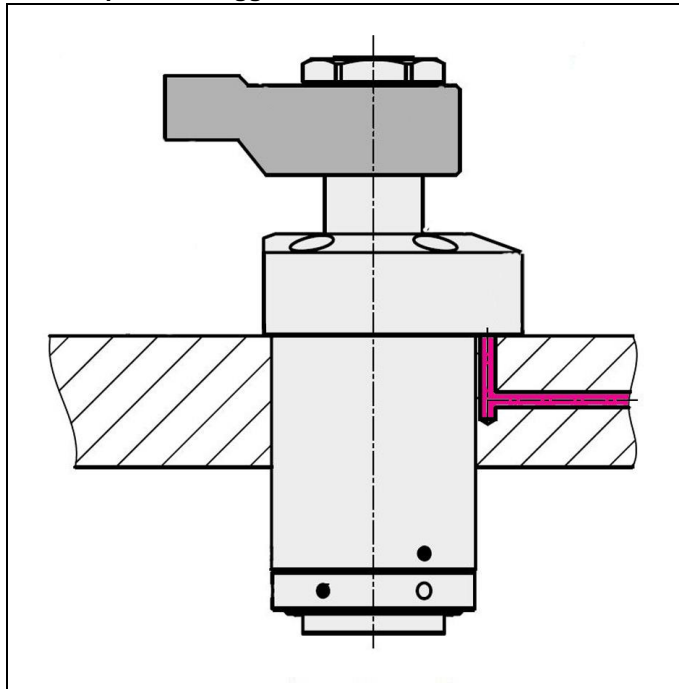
Versione con flangia, collegamento idraulico senza linea
